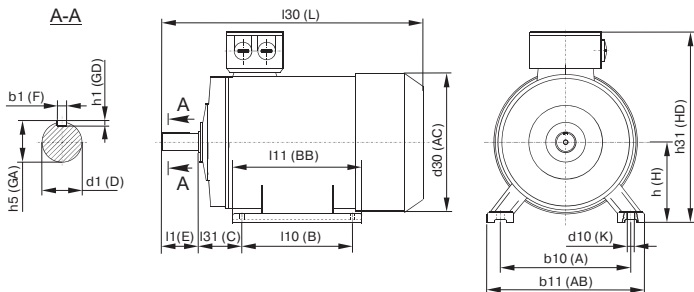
Размеры двигателей монтажного исполнения IM 1081, IM 1001 / Figure 1 – Motor dimensions of IM 1081, IM 1001 mounting version / Сурет 1 – IM 1081, IM 1001 монтаждық орындалым қозғалтқыштарының өлшемдері
